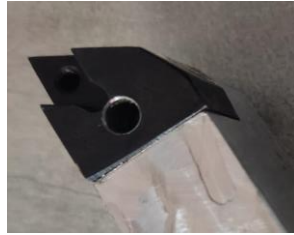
Porta inserto para la barra de Aluminio 7075T6
